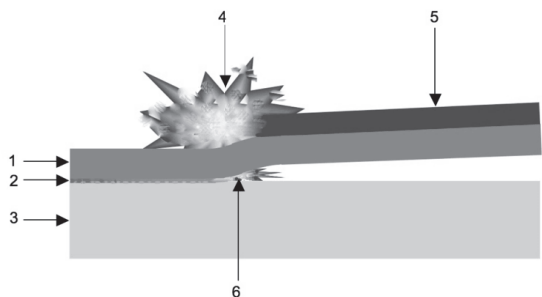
Схема сварки взрывом: 1 – метаемая деталь; 2 – сплавленная поверхность; 3 – неподвижная деталь; 4 – взрывная (ударная) волна; 5 – заряд взрывчатого вещества; 6 – кумулятивная струя
